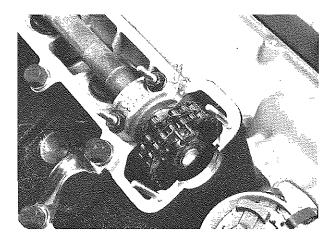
Smontaggio molletta di fermo Removing retaining spring
